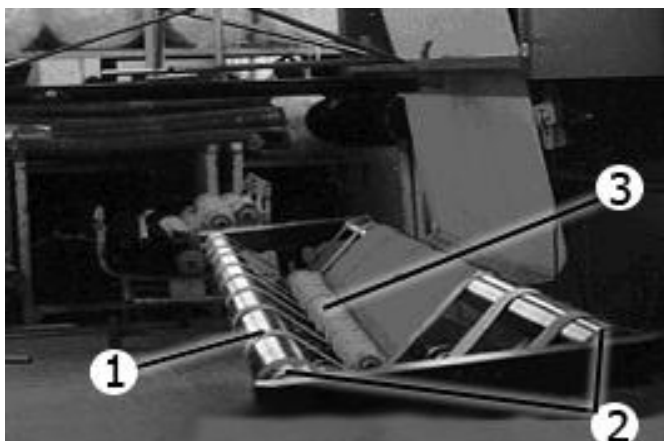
Конструктивная схема системы размотки: 1- приводные гибкие звенья; 2 - раздвижные консоли; 3-разматываемый рулон
